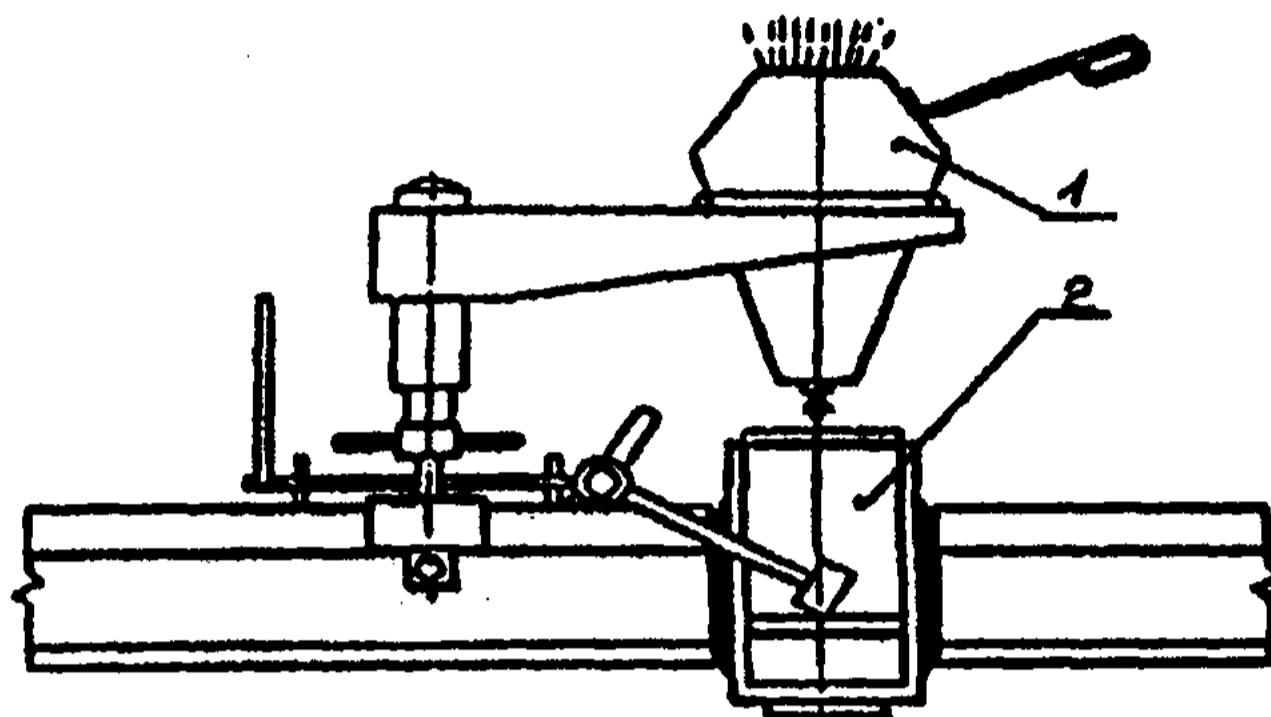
Схема установки формы и тигля в период кристаллизации металла сварного шва
